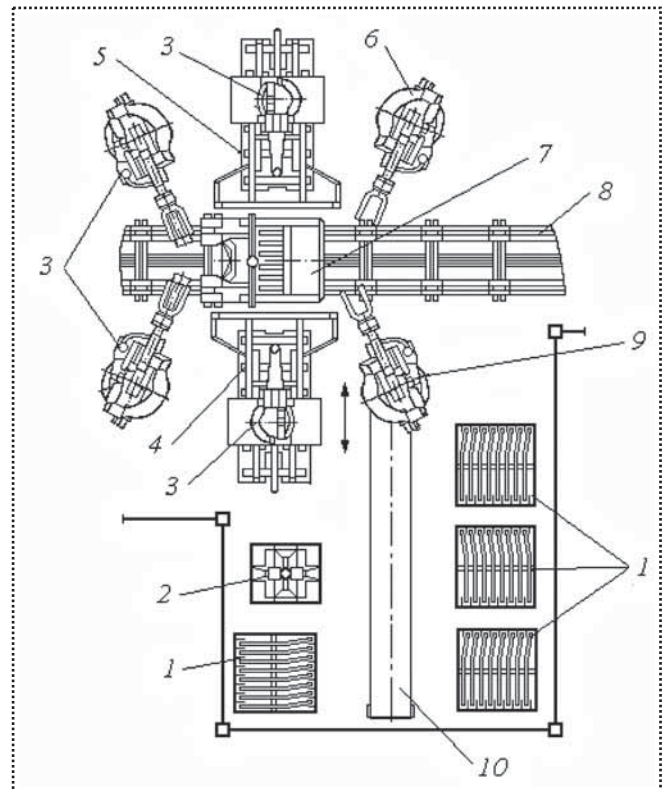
Компоновка роботизированного участка приварки левых и правых боковин к основанию кабины грузовых автомобилей в составе линии сборки-сварки автомобилей семейства "Газель"
